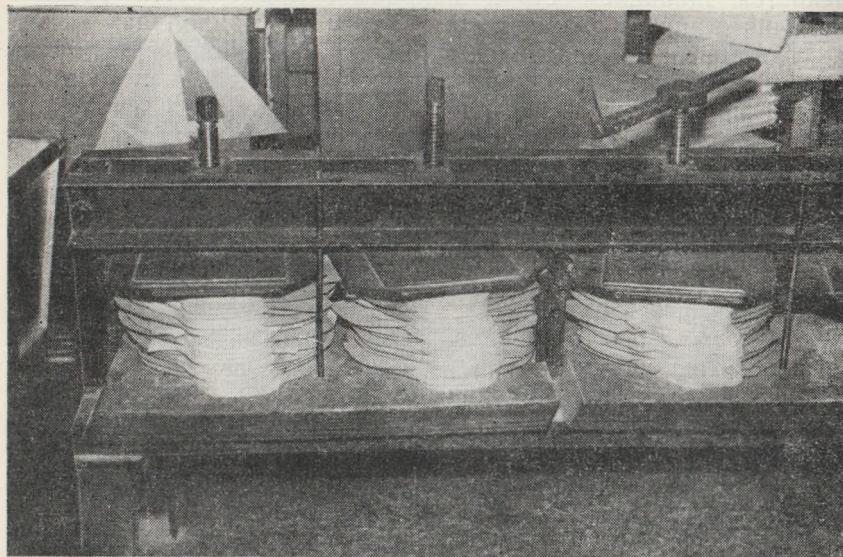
Винтовые прессы для запрессовки вкленных кружков, розеток и панцирей
